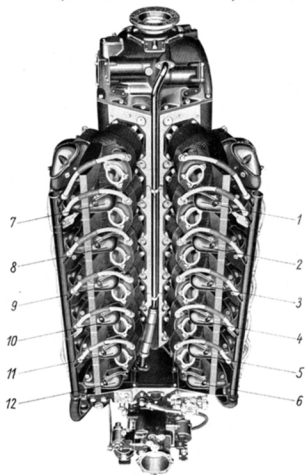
Zylinderreihenfolge (Motoransicht von unten)
